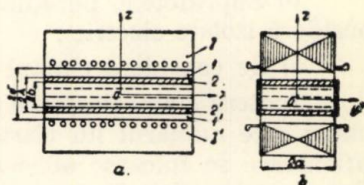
Secțiune transversală și longitudinală pentru pompa liniară plană.
